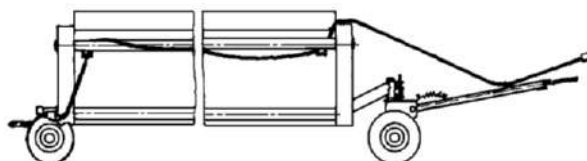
Схема прокладки жгута проводов по жатке
